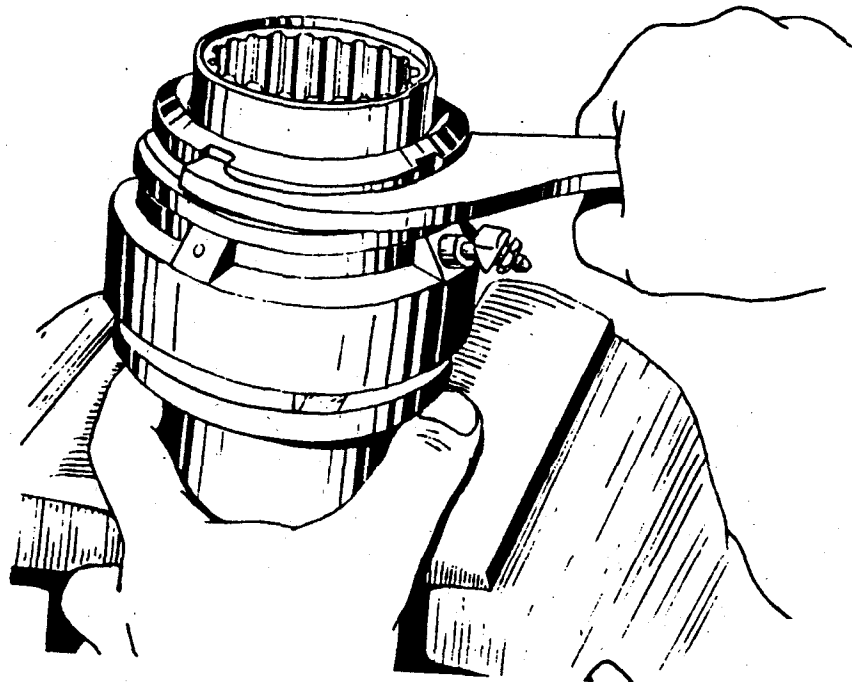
Отвертывание гайки крепления подшипника промежуточной опоры
